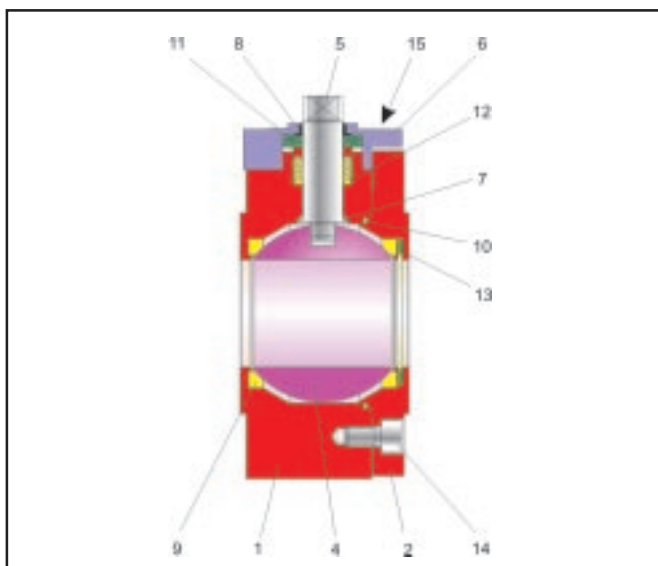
Schnittzeichnung des molchbaren Blockkugelhahns BR 28y
